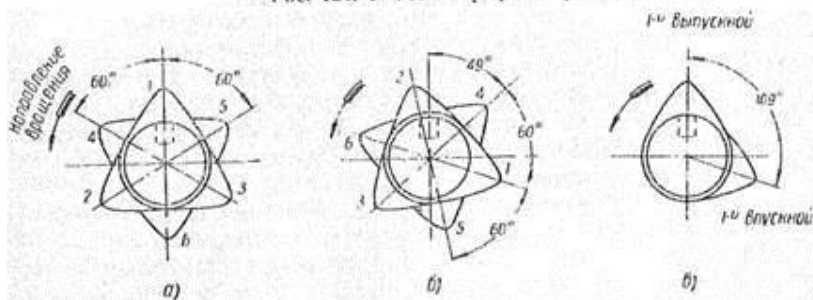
Схема углового расположения кулачков распределительного вала двигателей ГАЗ-51 и ЗИМ-12 (со стороны переднего конца вала): а — выпускные кулачки, б — впускные кулачки, в — кулачки первого цилиндра.
